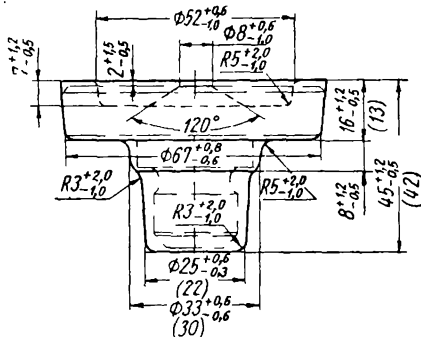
Чертеж поковки, изготавливаемой в закрытом штампе. Штампочные уклоны  $1^\circ$ ; неуказанные радиусы закруглений  $R = 1,5$  мм; допускаемый торцовый заусенец до 5 мм
